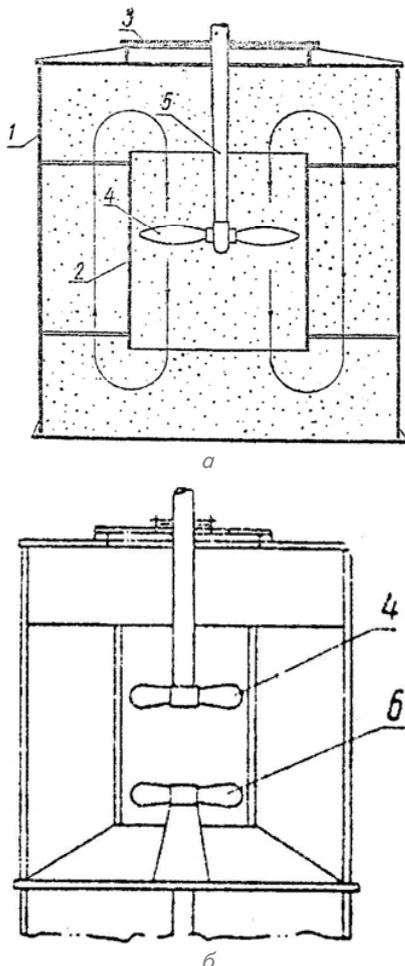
Схема устройства для шлифовки и полировки воздушных винтов [5]:
